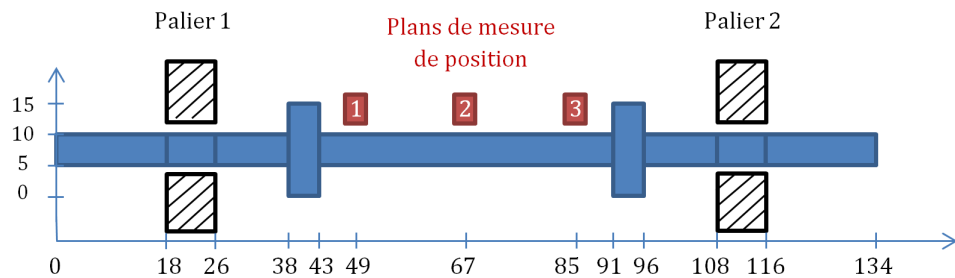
Représentation schématique des dimensions géométriques du rotor (mm)
